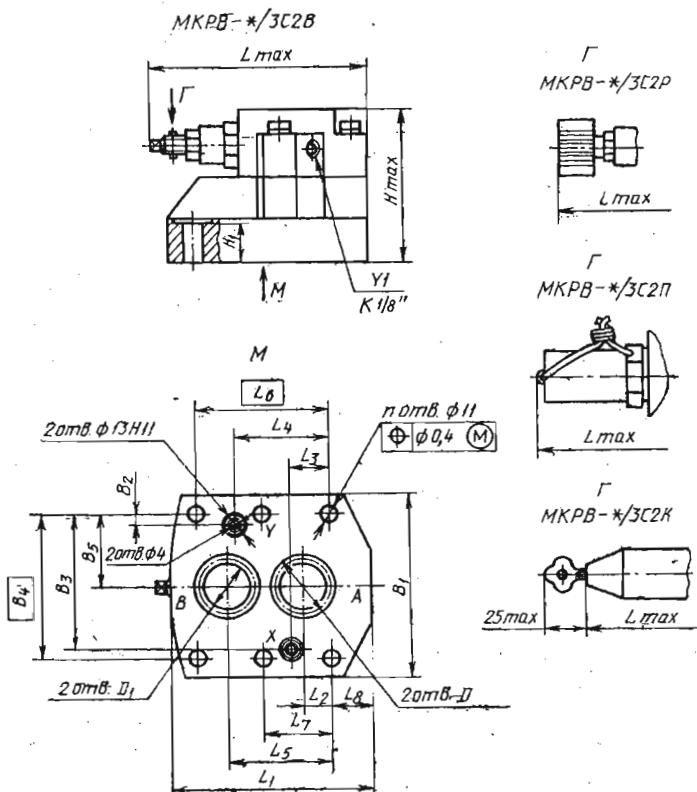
Габаритные и присоединительные размеры гидроклапанов редукционных стыкового монтажа типа МКРВ-*/3С2
